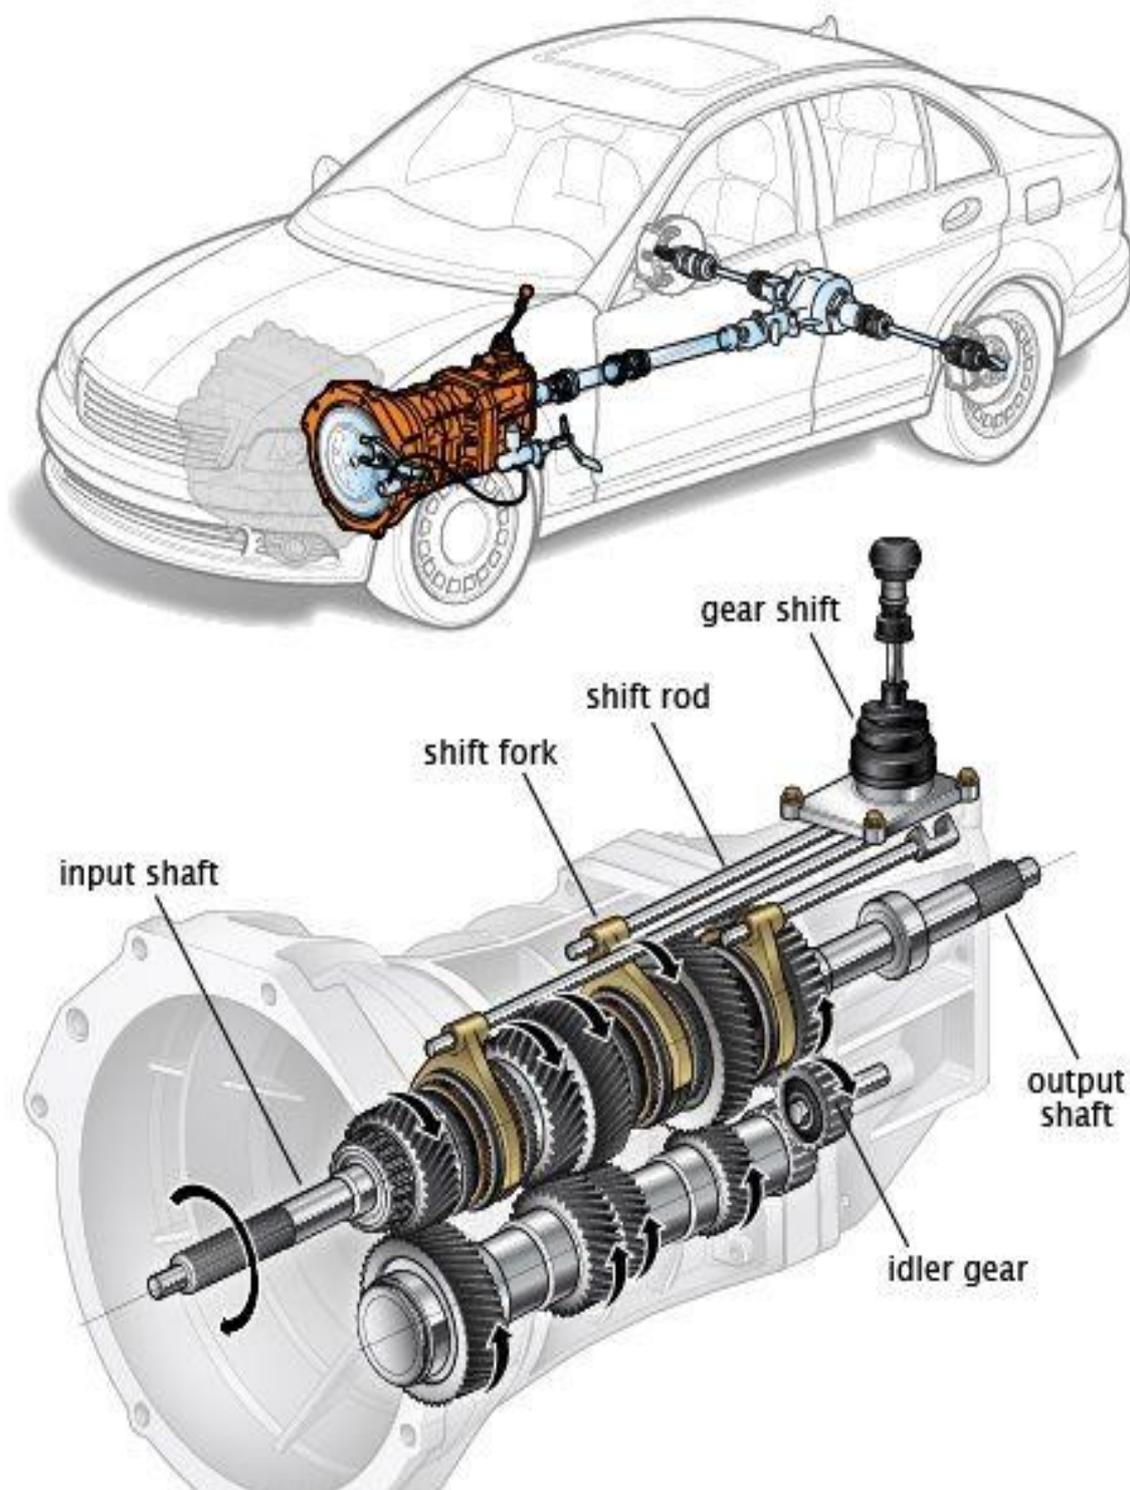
Vue d'ensemble de la boîte vitesse [12].
